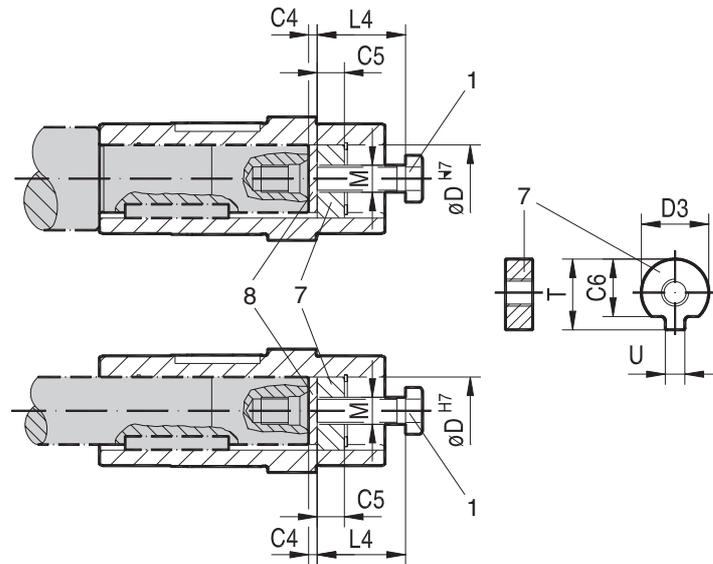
Kit de montaje y desmontaje de SEW-EURODRIVE
